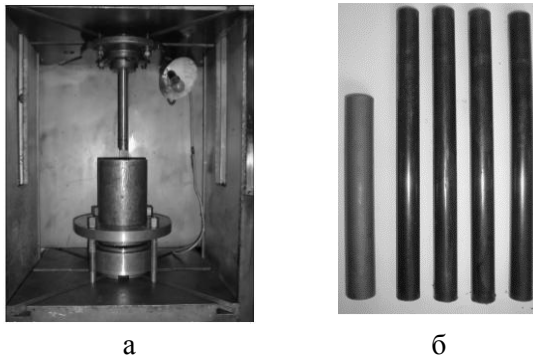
Фотографії штампа на пресі, вихідна заготовка і отримані стержні
